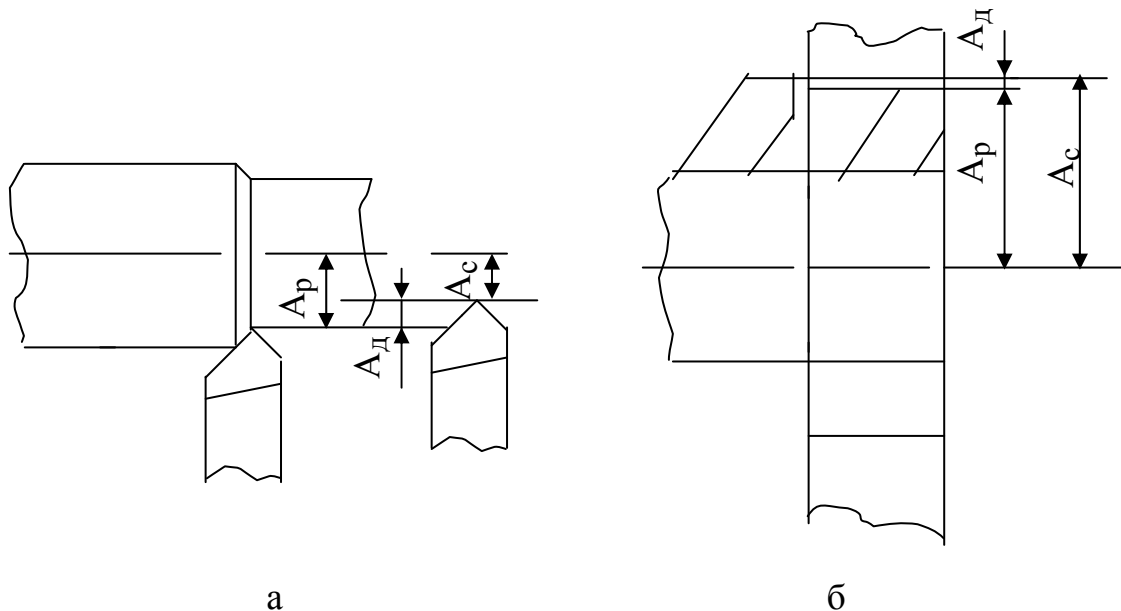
Определение размера статической настройки  $A_c$ , который обеспечит требуемый рабочий настроечный размер  $A_p$  при обработке охватываемой (а) и охватывающей (б) деталей.
